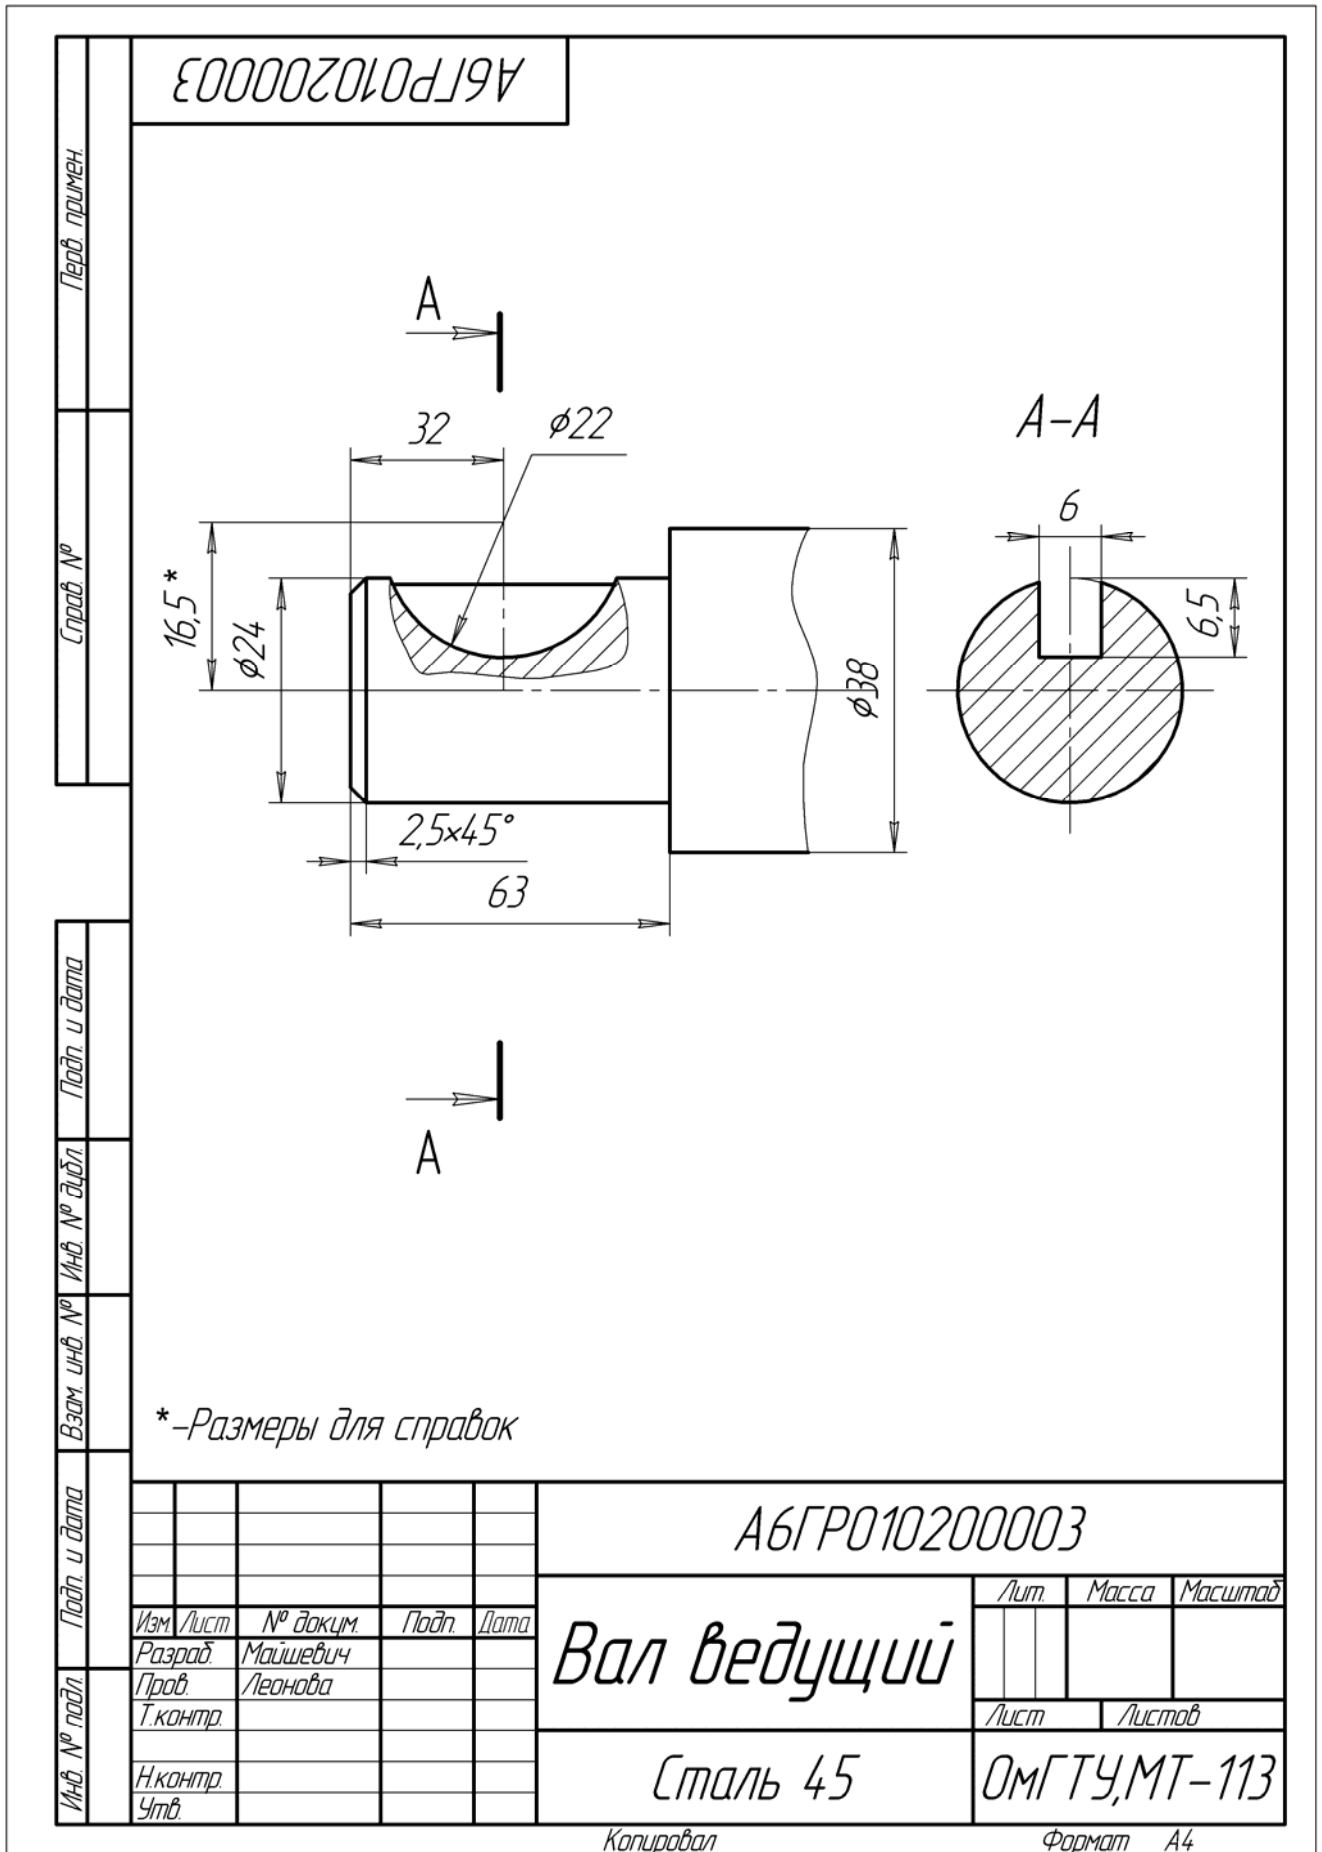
Рабочий чертеж хвостовика ведущего вала
